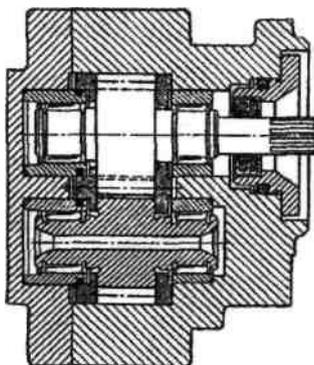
Шестеренный насос с плавающими втулками и игольчатыми подшипниками
